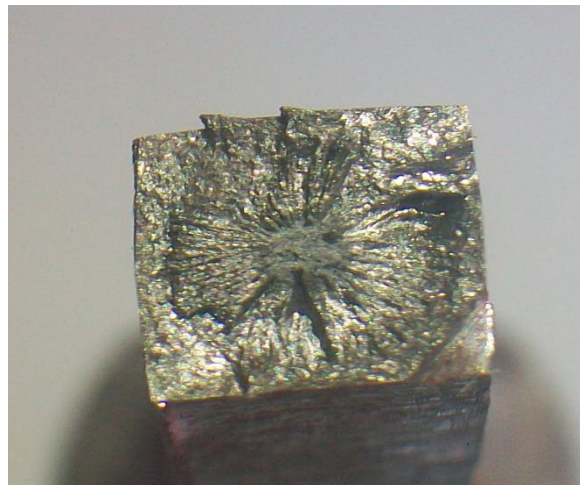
Sección transversal de la rotura de la probeta 3.
